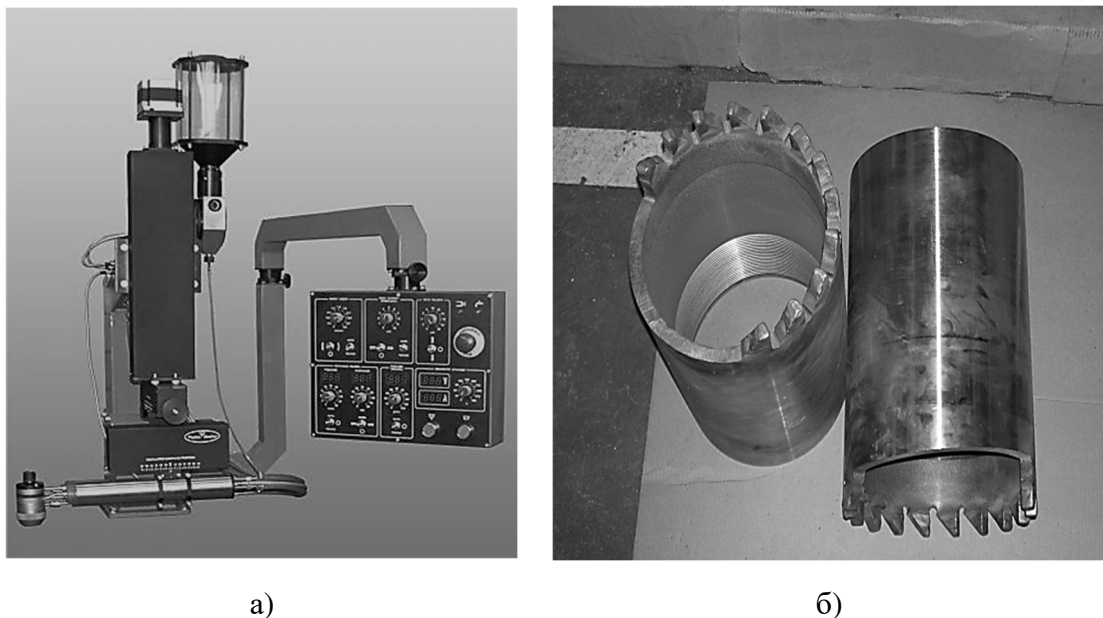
Аппарат для плазменно-порошковой наплавки (а), наплавка зубьев – (б)
